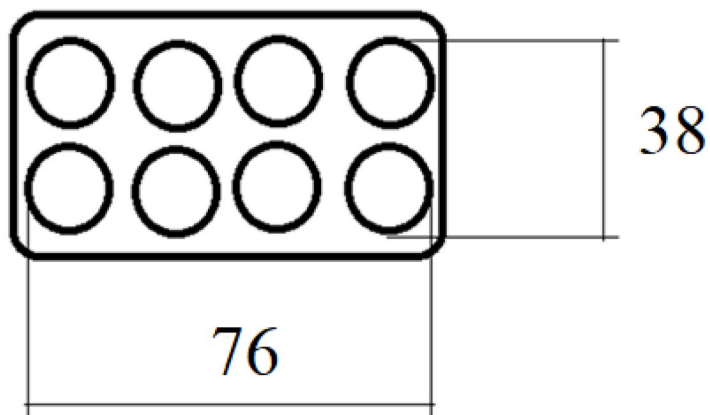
Размеры конденсатора из 8 секций в мм вид сбоку
